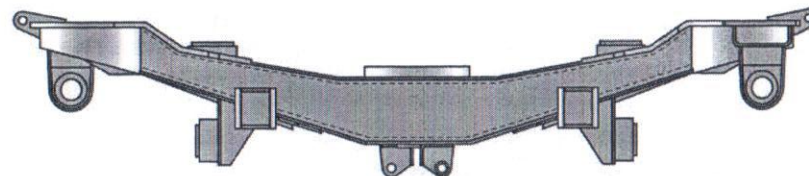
Контроль околошовных зон сварного соединения боковой стенки с верхней и нижней пластинами
